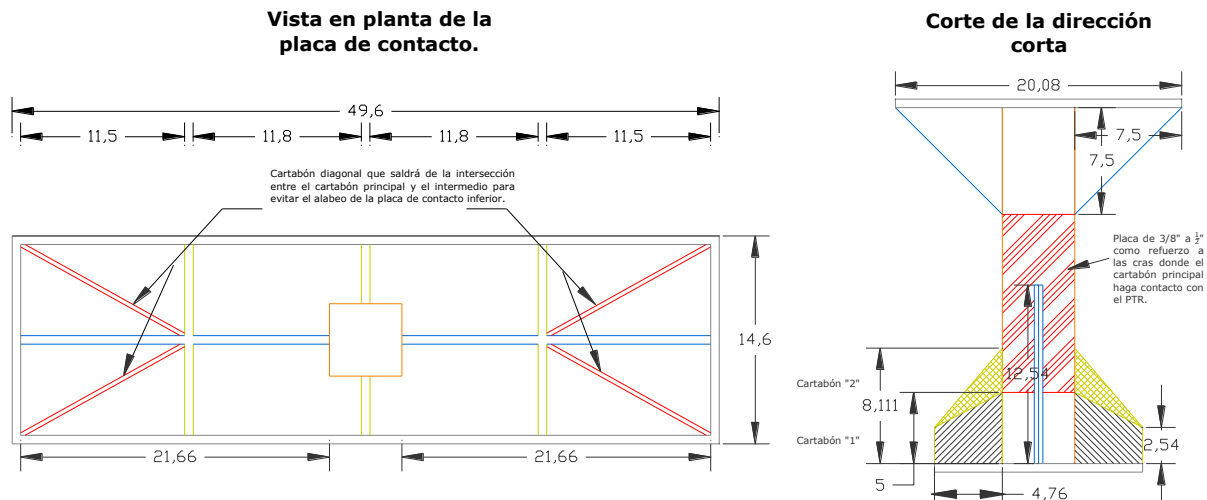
Vista en planta y en elevación del lado corto del pisón estático
